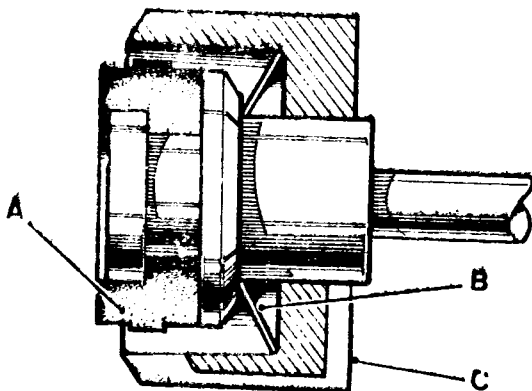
13 - Montaje de la empaquetadura de la válvula.
